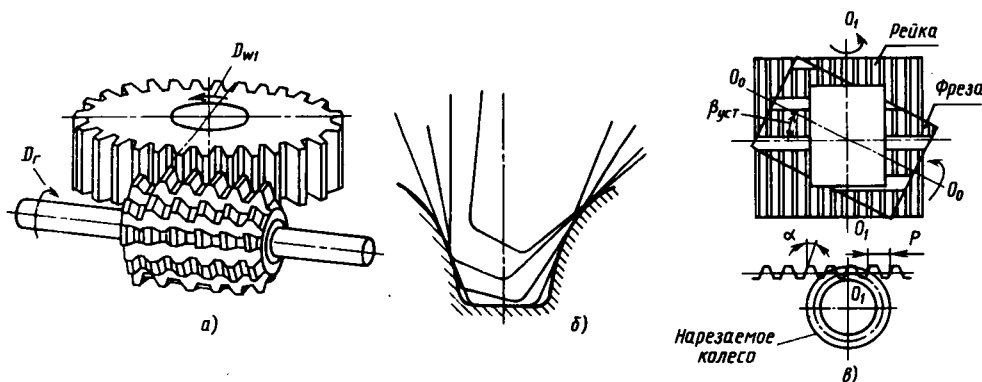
Схема работы червячной фрезы (а и в) и образование профиля зубьев колеса (б)
